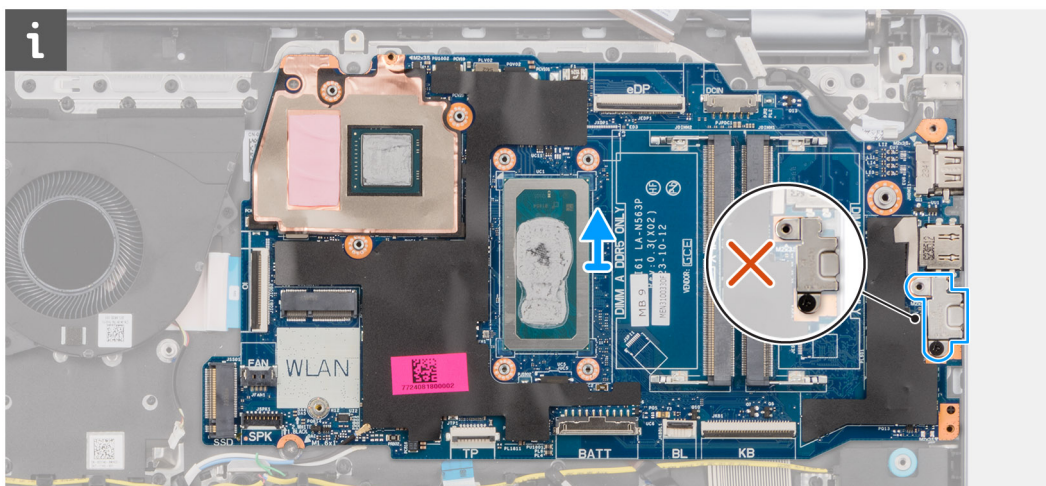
Tarjeta madre: soporte para USB Type-C
